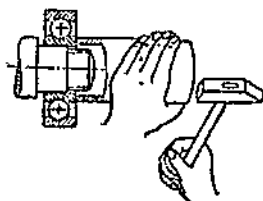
Постановка на вал шарикоподшипника при помощи деревянного клина.
